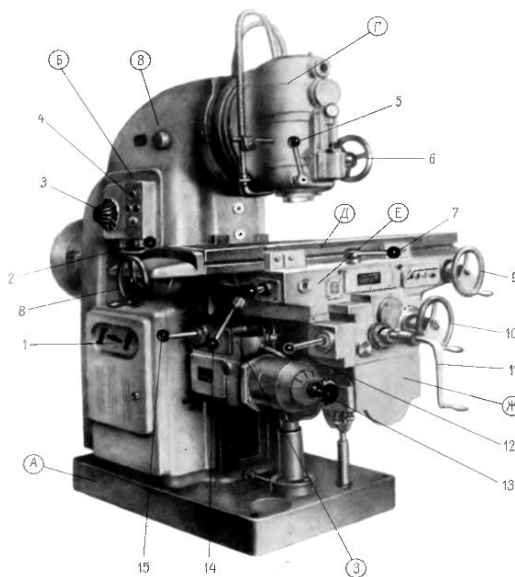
Вертикально-фрезерный станок модели 6Н12ПБ
